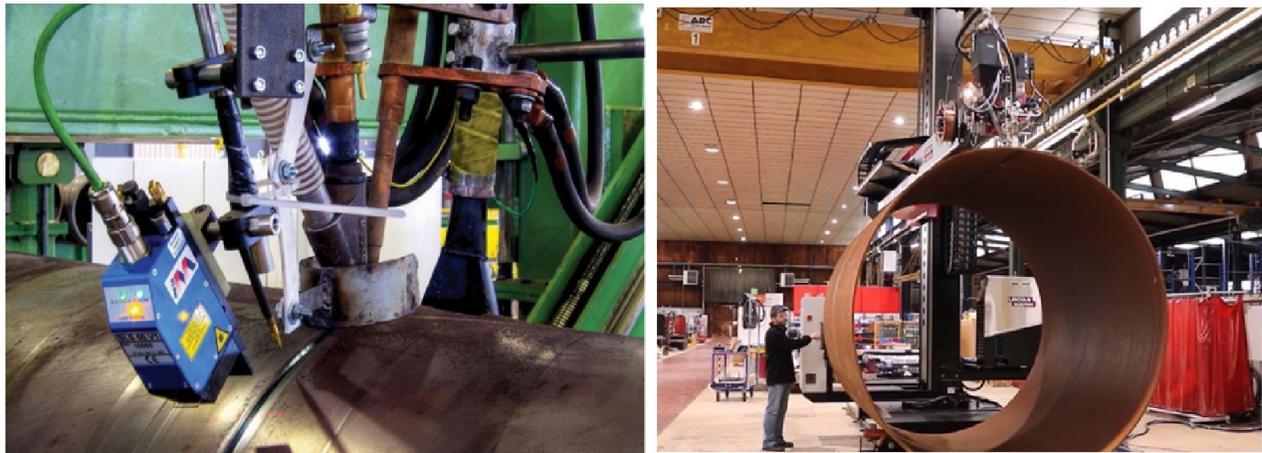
Equipo para soldadura en formato cilíndrico.
